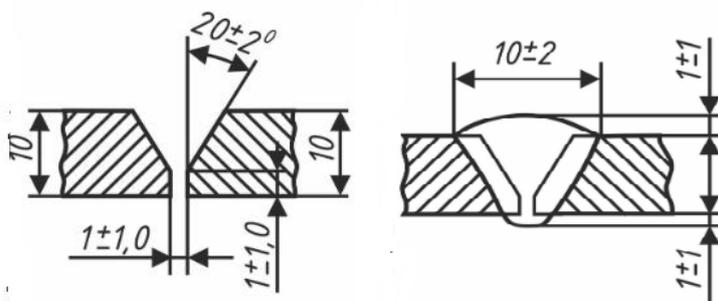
Конструктивные элементы и размеры сварного шва С17
